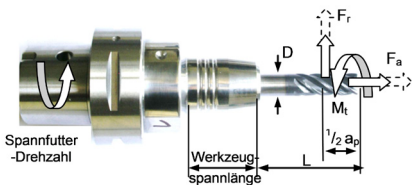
Kräfteangriff an einem HM-Schaft-Werkzeug bzw. Spannfutter
